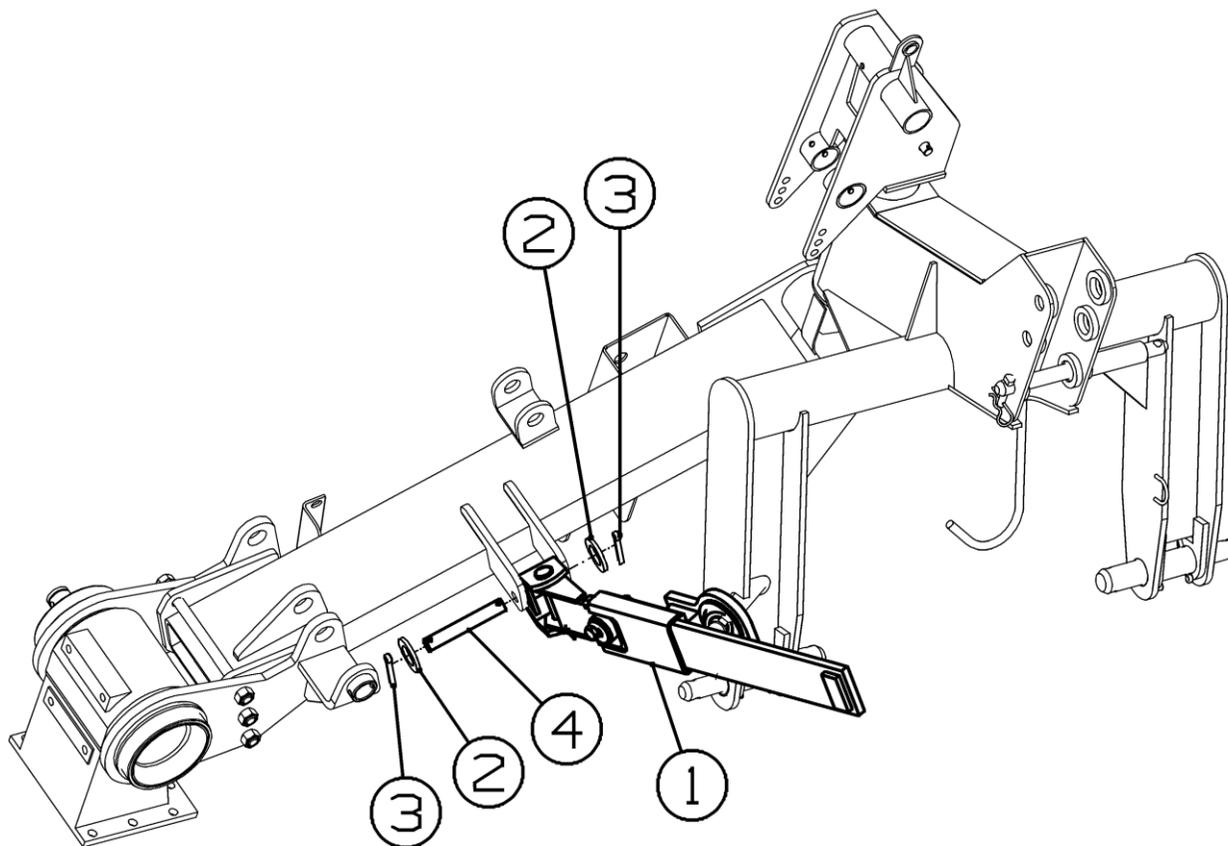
КРН - 2.8.06.000 Установка предохранителя
